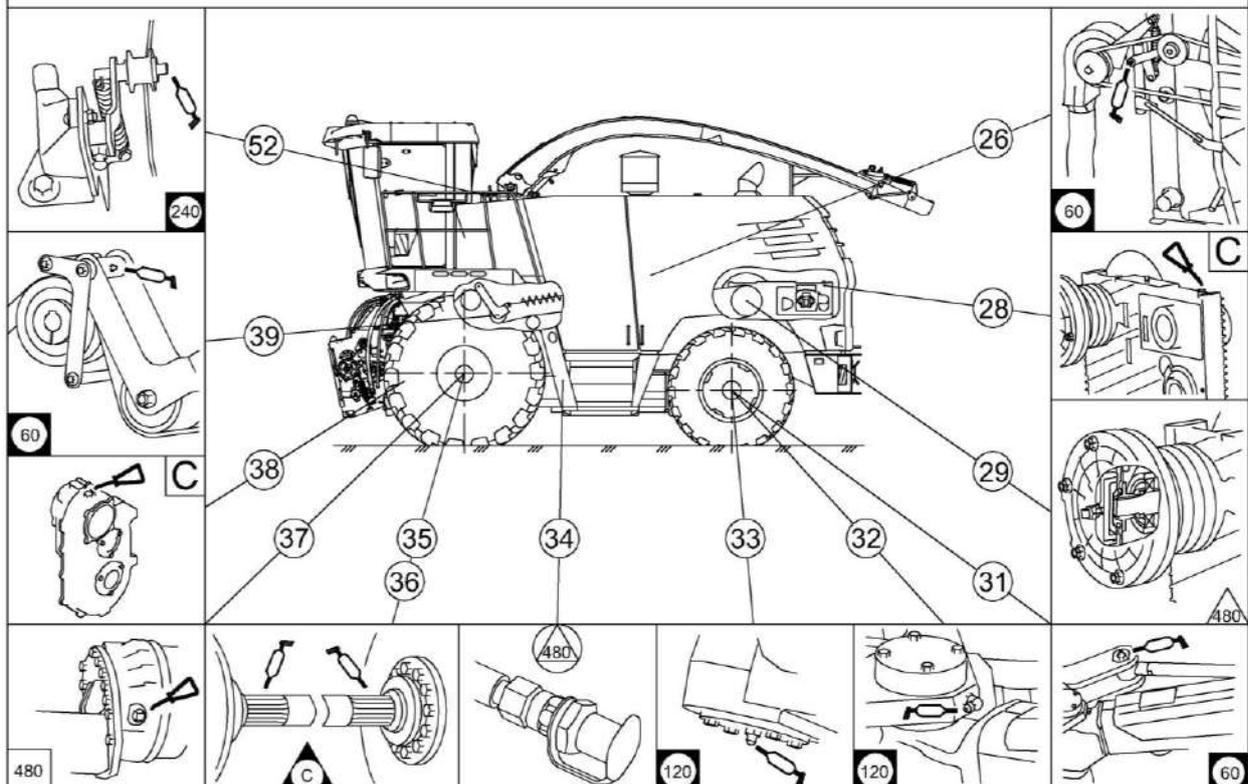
Схема смазки комбайна (вид слева)
